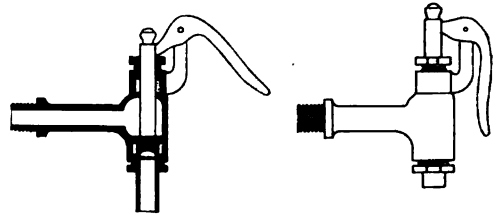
Eckauslaufhahn Roover, geschlossen. geöffnet.
